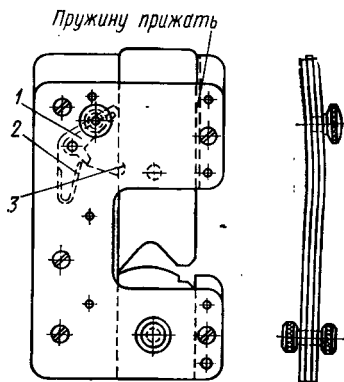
Рамочный шаблон для контроля профилей лопаток
